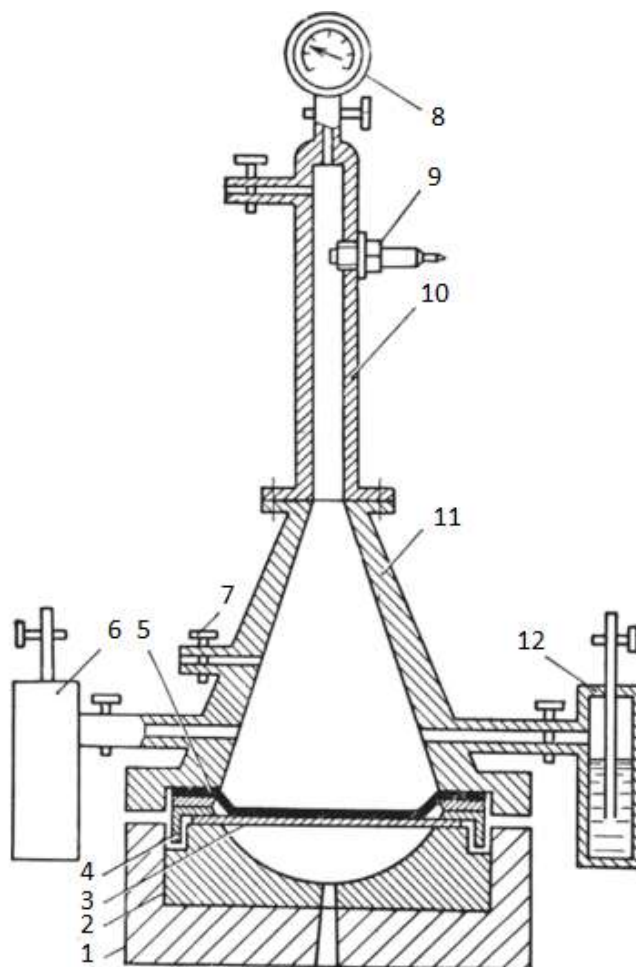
Схема установки для штампування вибухом газової суміші:
